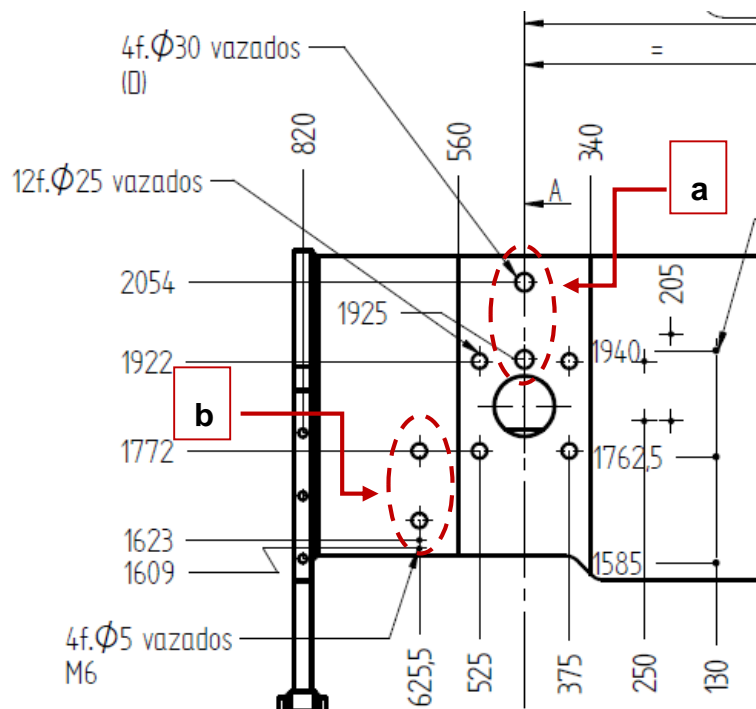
Desenho parcial da vista frontal da estrutura da máquina BB5020 (versão D) com destaque para as interfaces das tubeiras do redutor (a) e do lubrificante (b).
